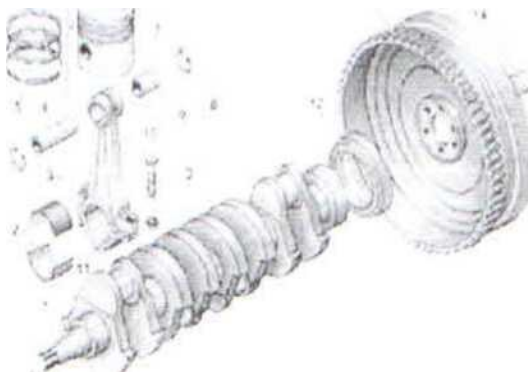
Коленчатый вал и детали шатунно-поршневой группы
